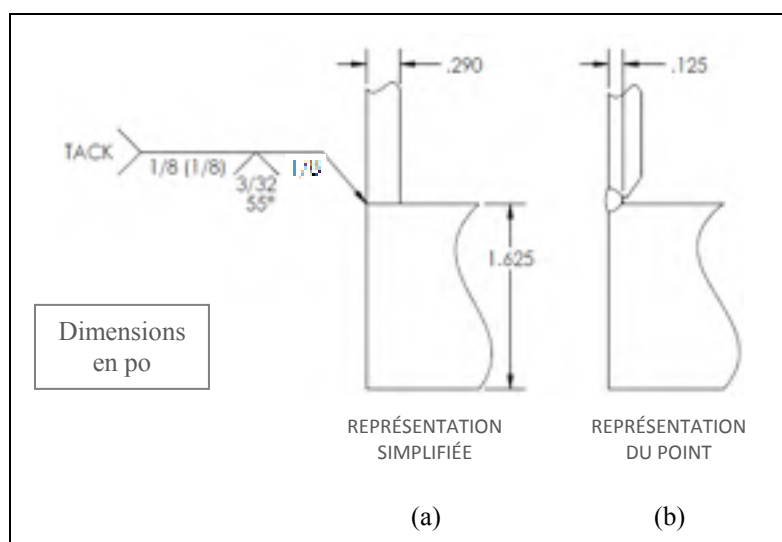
Configuration du joint soudé par point typique pratiqué sur la structure
